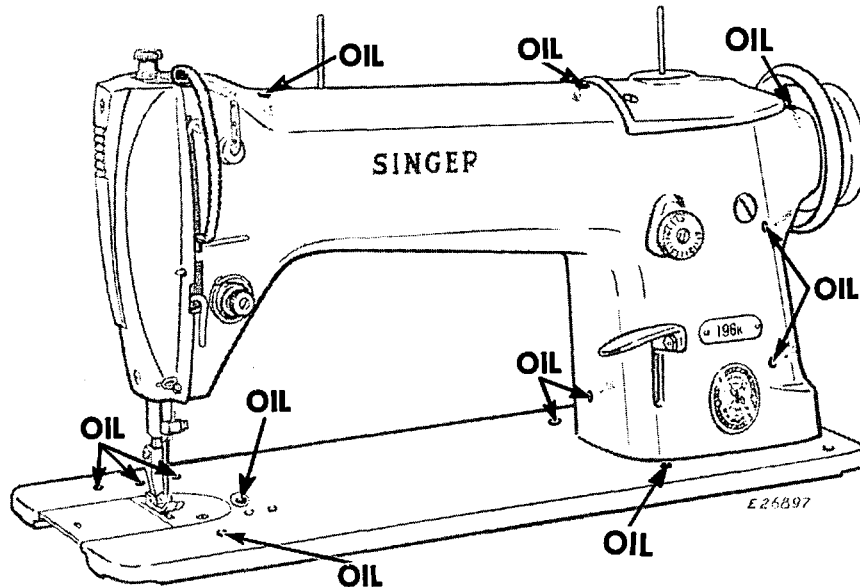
Points de graissage à l'avant de la Machine 196K5
